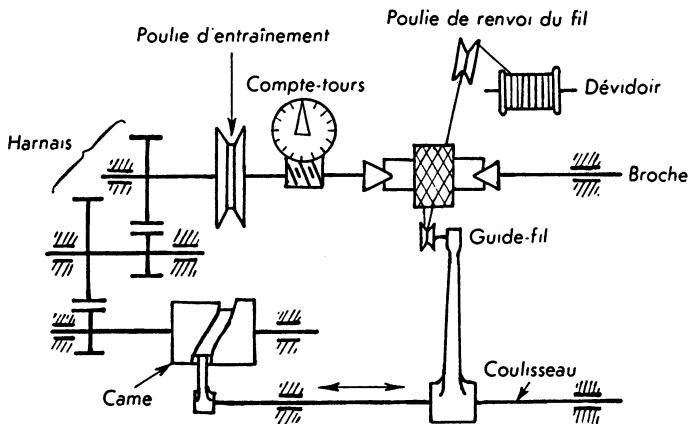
Machine à bobiner en nid d'abeilles
